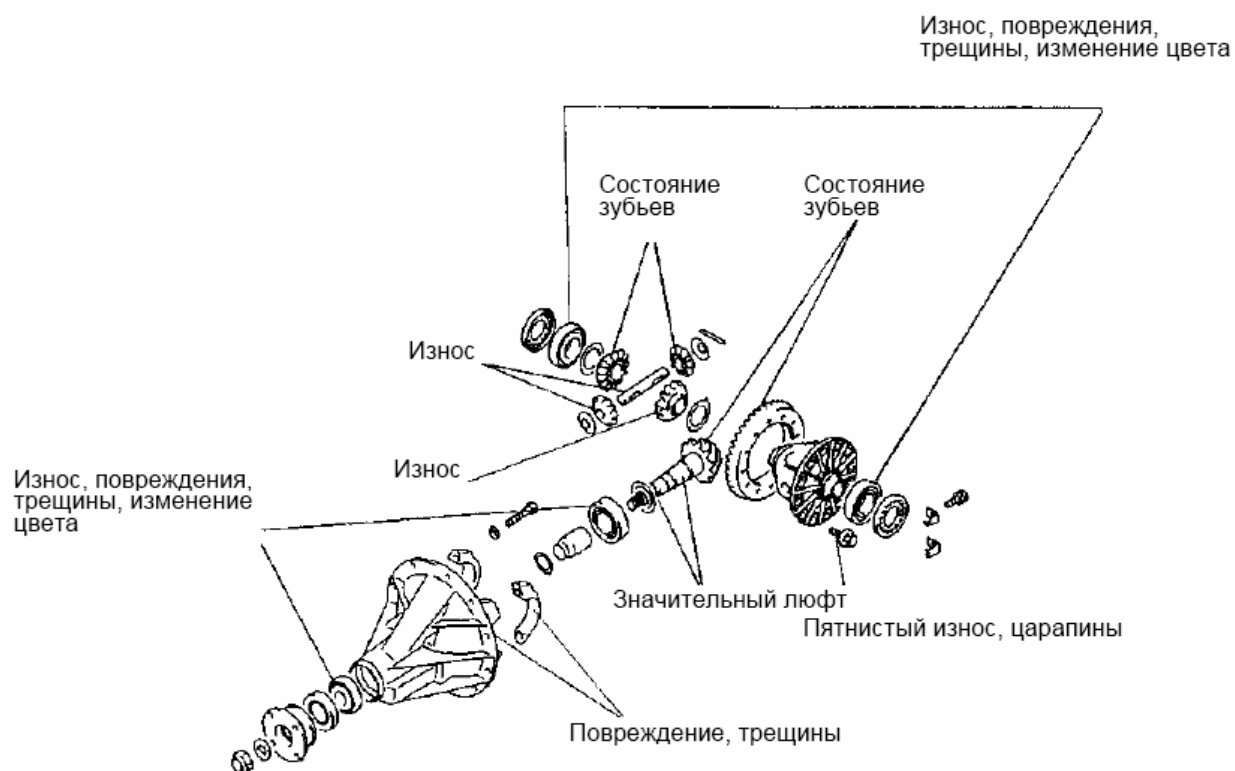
Проверка деталей главной передачи и дифференциала после разборки
